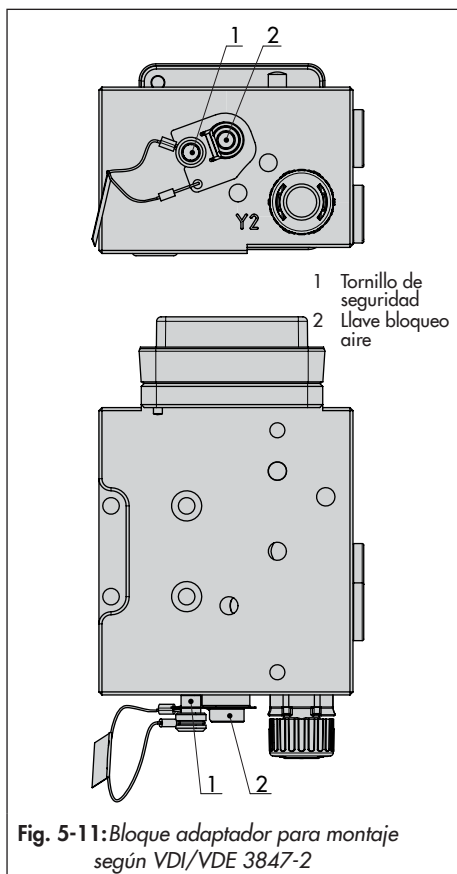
Bloque adaptador para montaje según VDI/VDE 3847-2
